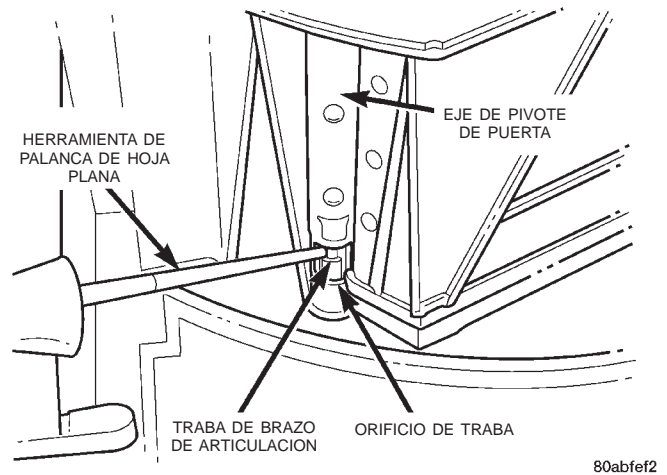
Desmontaje e instalación de la palanca de puerta de modo - Característico
